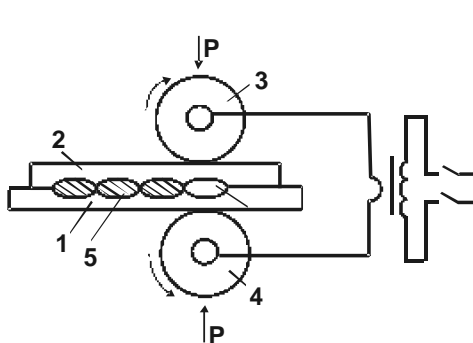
Схема роликоче зварювання: 1, 2 – деталі; 3, 4 – електроди; 5 – ядро металу шва
